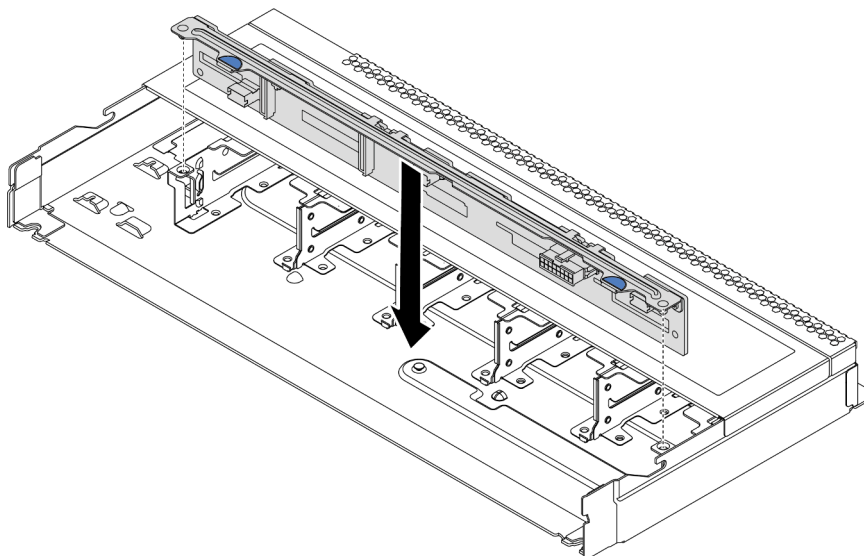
Installation du fond de panier pour dix unités remplaçables à chaud 2,5 pouces
